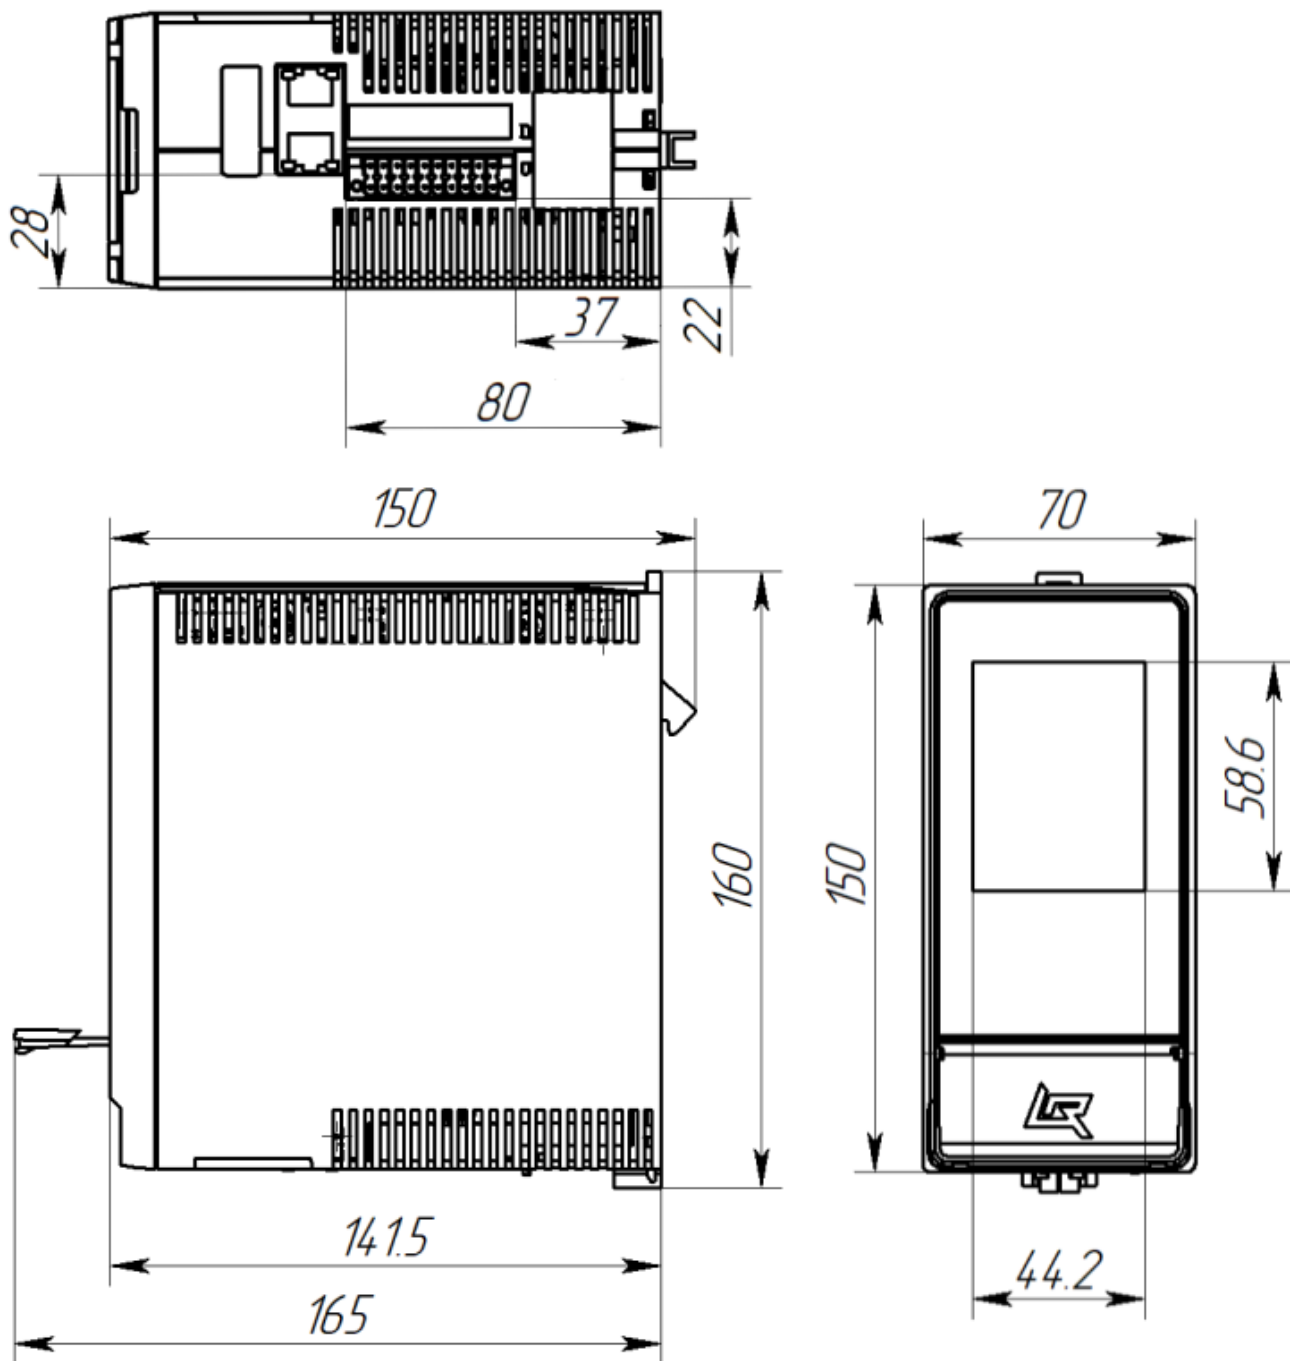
Габаритные и присоединительные размеры модуля ЦПУ в пластмассовом корпусе
